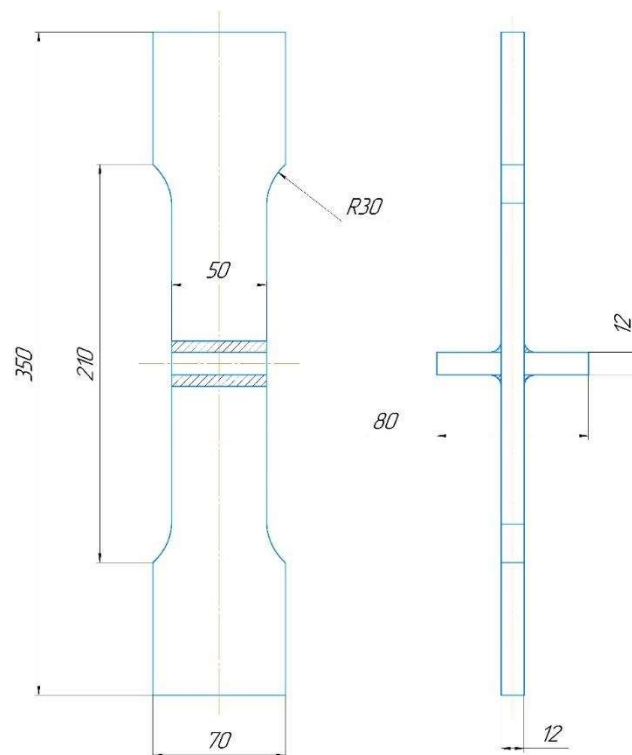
Схема зразка таврового зварного з'єднання з двома поперечними ребрами
